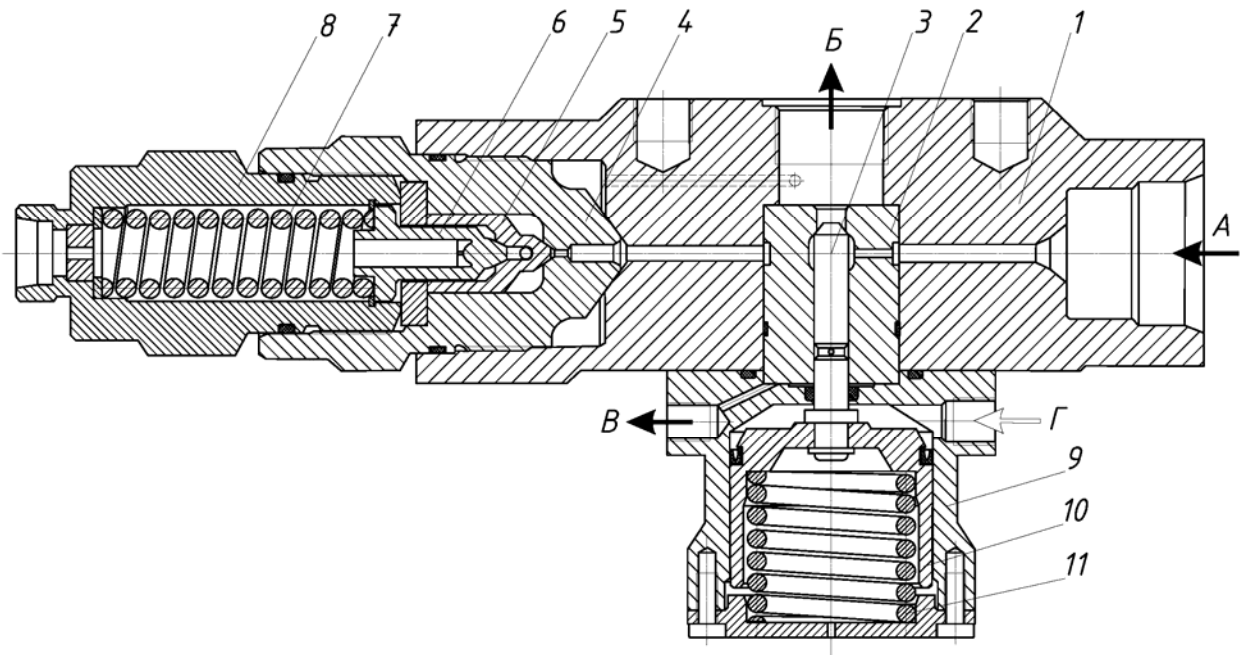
Клапан прокачування і аварійного скидання тиску і клапан обмеження максимального тиску. 1 – корпус блоку клапанів; 2 – корпус клапана прокачування; 3 – шток клапана прокачування із запірним конусом; 4 – корпус клапана-обмежувача максимального тиску; 5 – вставне сидло клапана-обмежувача; 6 – запірний конус клапана-обмежувача; 7 – навантажувальна пружина; 8 – різьбова пробка; 9 – пневматичний циліндр приводу клапана прокачування; 10 – поршень приводу клапана прокачування; 11 – навантажувальна пружина. А – підведення палива від акумулятора; Б – зливна магістраль; В – збір протікань; Г – стиснене повітря з системи управління
